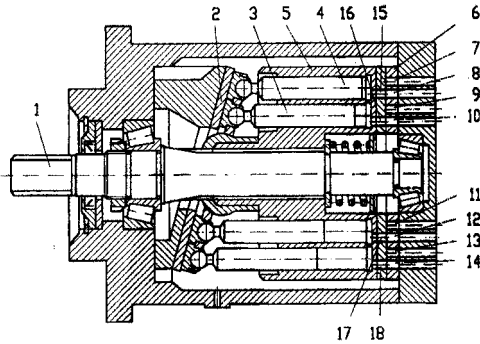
Аксиально-поршневая гидромашинa с двухрядным блоком цилиндров и модернизированным опорно-распределительным диском: 1 – ведущий вал; 2 – наклонная шайба; 3, 4 – поршни; 5 – блок цилиндров; 6 – опорно-распределительный диск; 7...14 – полукольцевые пазы; 15...18 – канал
